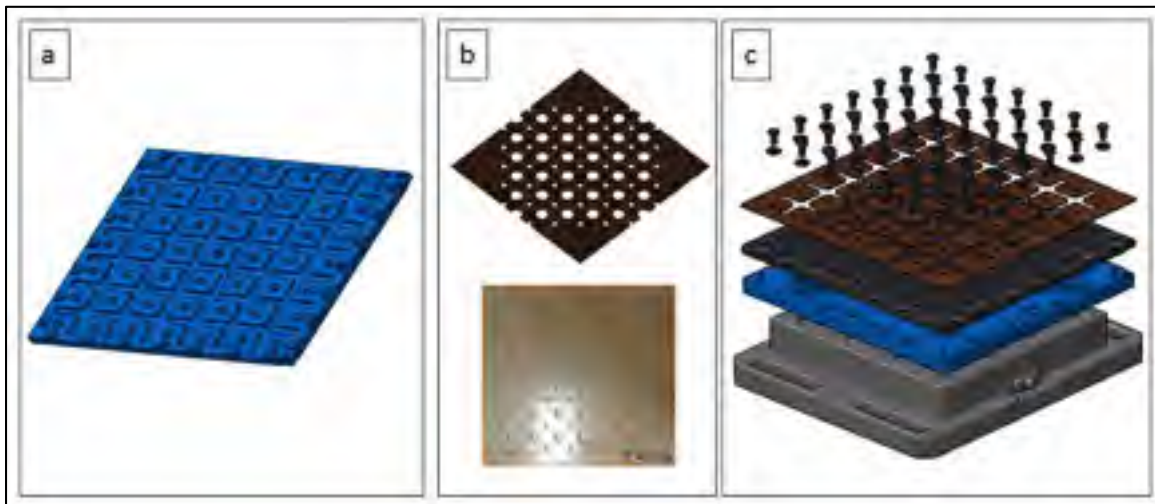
Montage de découpe : a) vue du gabarit de détournage, b) patron de perçage de la plaque et c) vue explosée du montage avec la plaque et les vis de serrage
